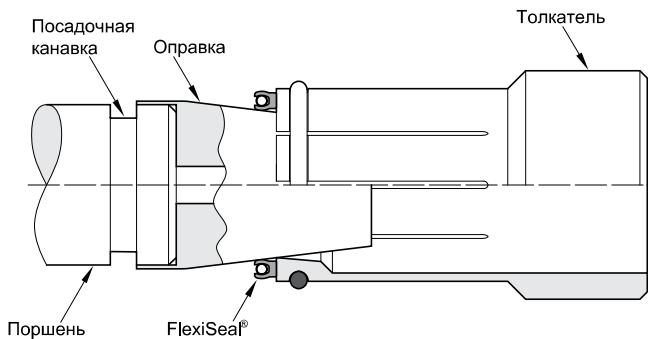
Растягивающий направляющий конус, толкатель и инструмент для изменения размера.
